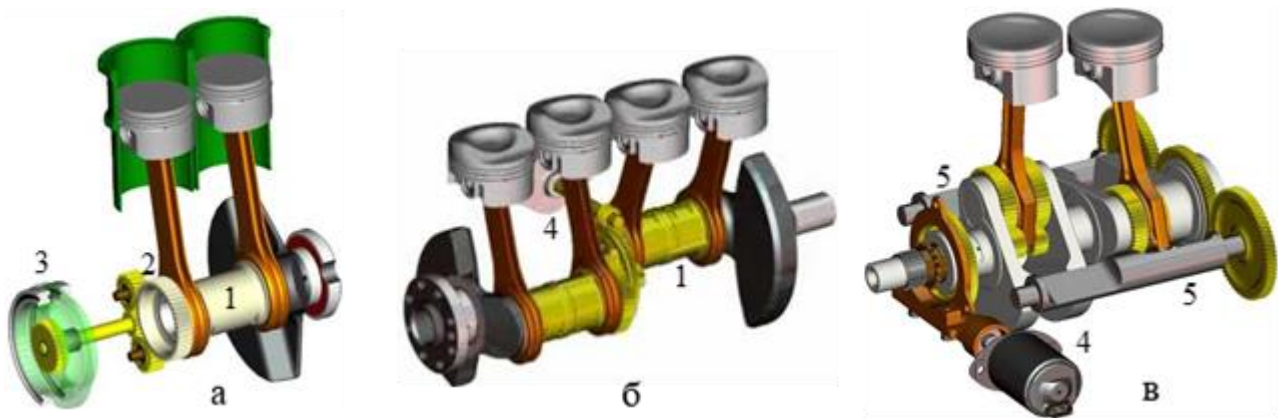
Конструкції двигуна VCR Go Engine з ексцентриковими валами:
